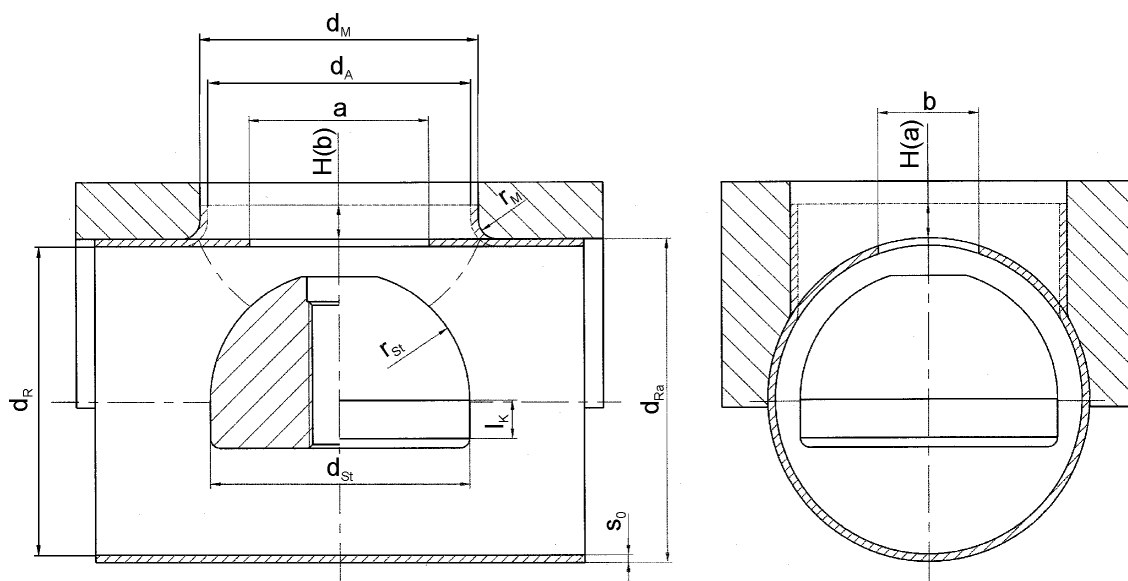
Geometrische Werkzeug- und Werkstückengrößen
